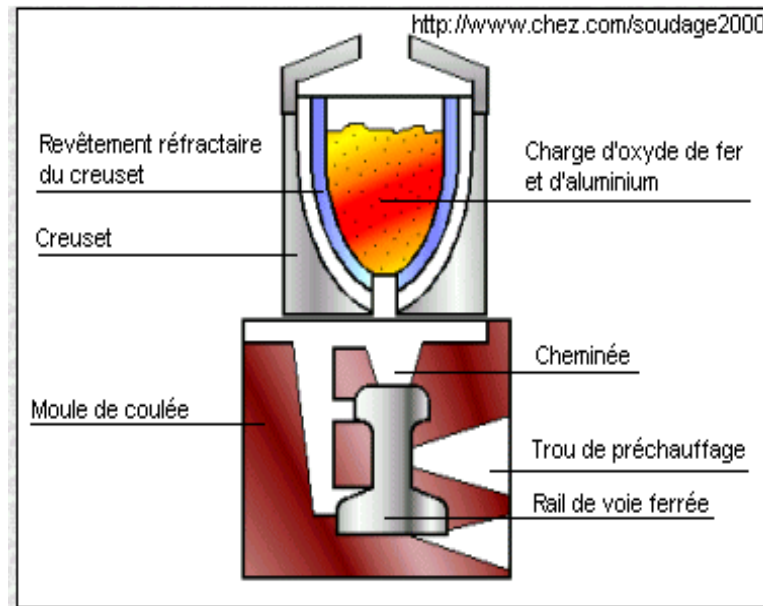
Principes de la soudure aluminothermique. [2]
